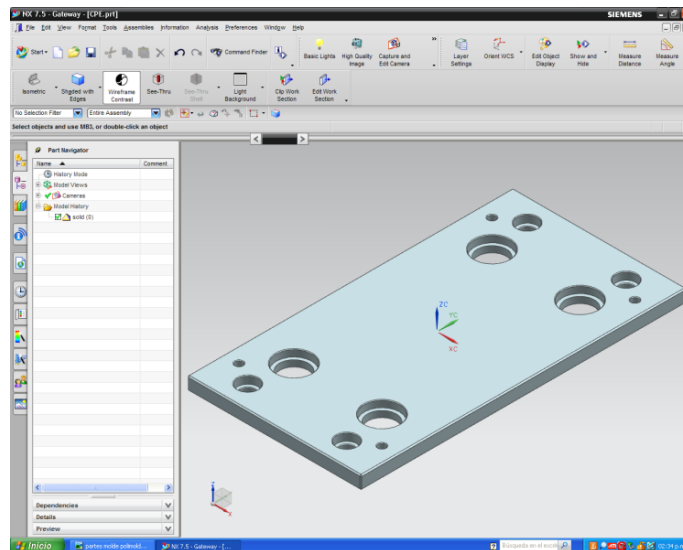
Placa limitadora de botadores CPE, vista isométrica.
